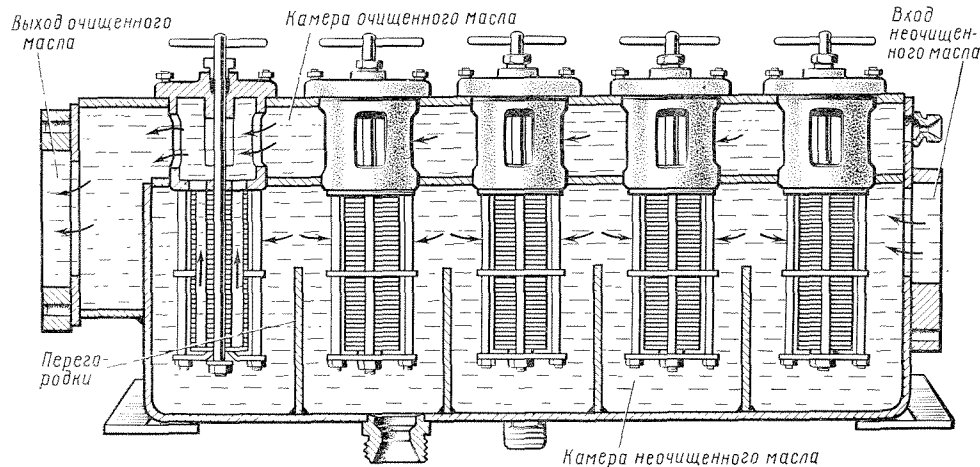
Корпус фильтра грубой очистки масла и его камеры
